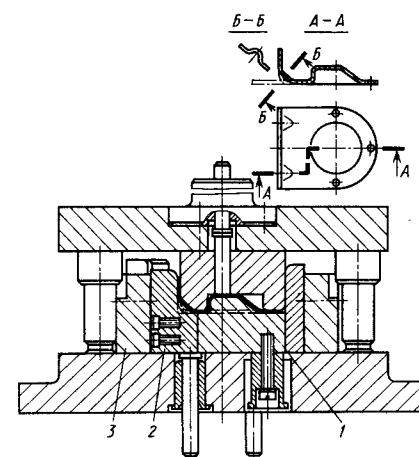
Штамп для гибки полки детали в заготовке, ранее подвергнутой вытяжке
